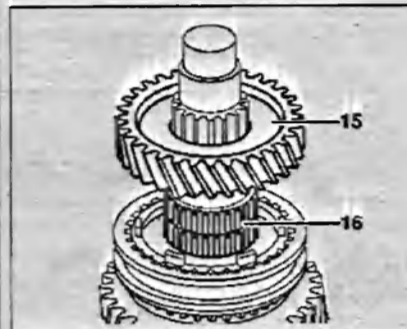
Снимите шестерню 15 2-й передачи и игольчатый подшипник 16.
